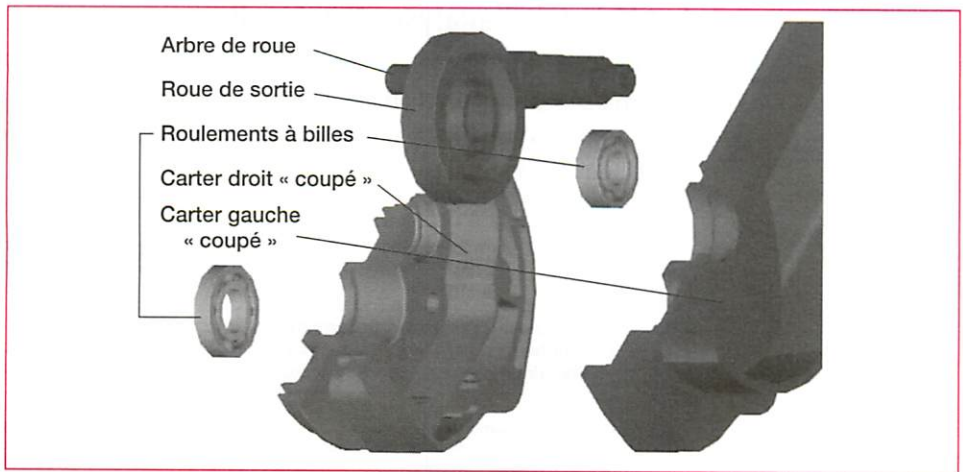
Guidage en rotation de l'arbre de roue en vue éclatée
